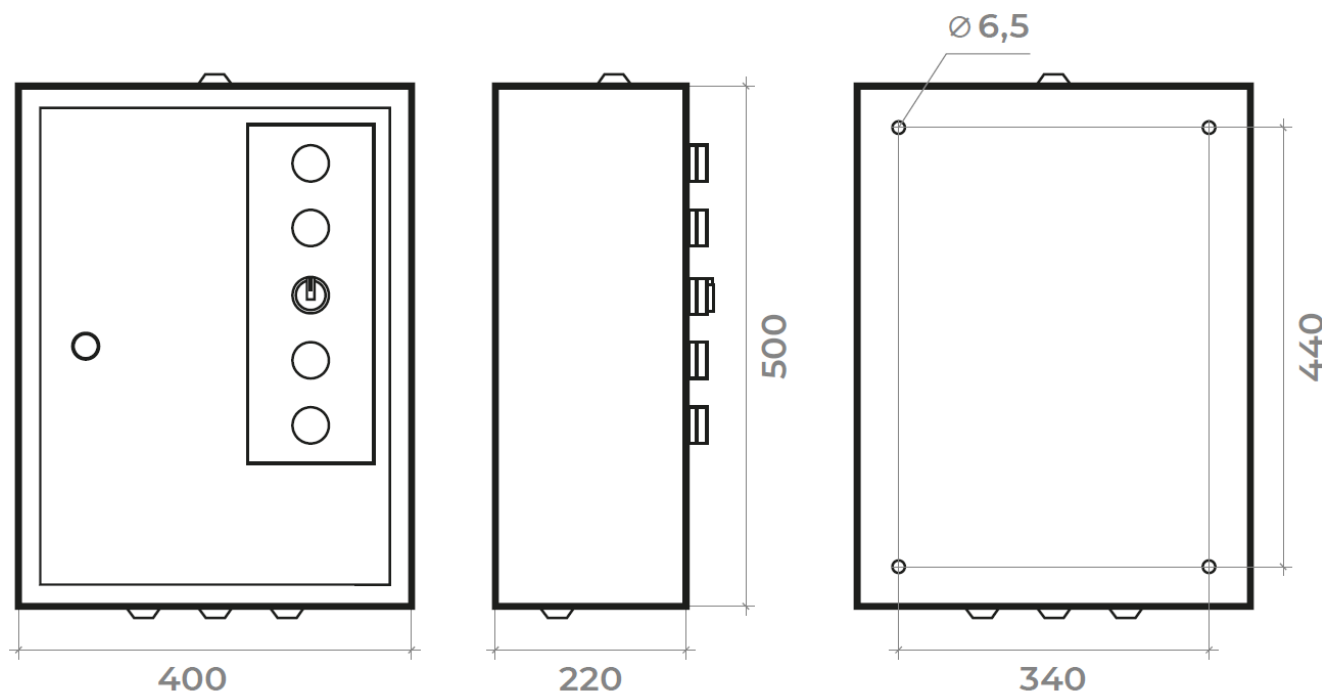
Габаритные и установочные размеры ШУВ-30/ШУВ-45.
